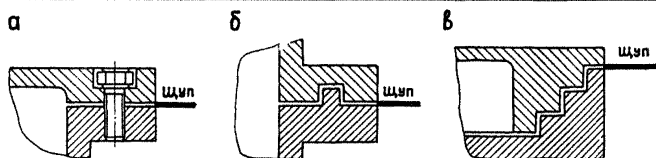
Способы контроля ширины щели (зазора) во фланцевых соединениях:
